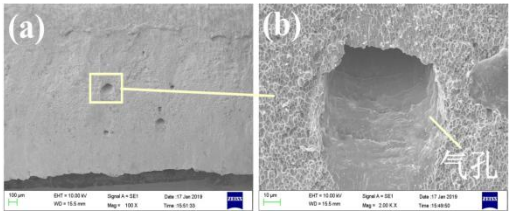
焊接速度为 0.8 m/min 时拉伸试样断口形貌图：
